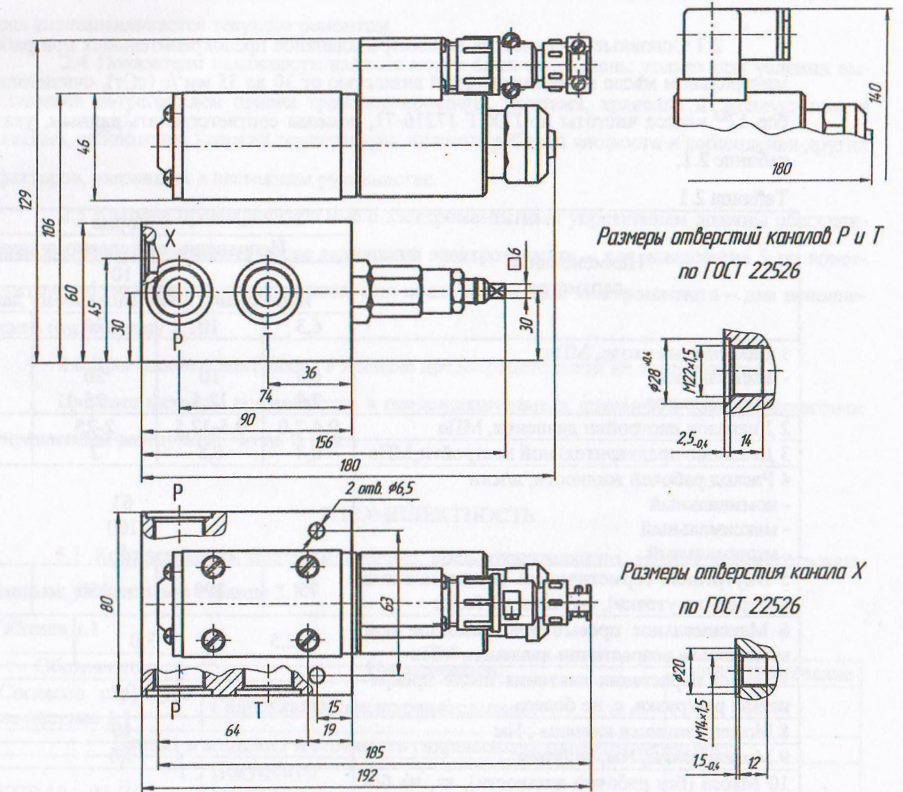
Габаритные и присоединительные размеры клапана предохранительного типа КПР 10/X TXX - XX
